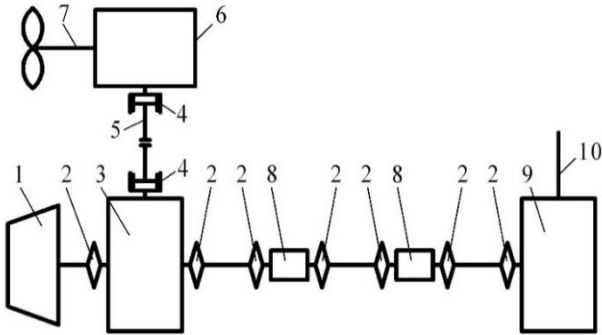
Кінематична схема трансмісії судна з ГТА: 1 – ТГ; 2 – пружні дискові муфти; 3 – редуктор; 4 – ЗМ; 5 – торсіонний вал; 6 – редуктор повітряного гвинта; 7 – вал повітряного гвинта; 8 – проміжна опора; 9 – редуктор гвинта; 10 – вал вентилятора
